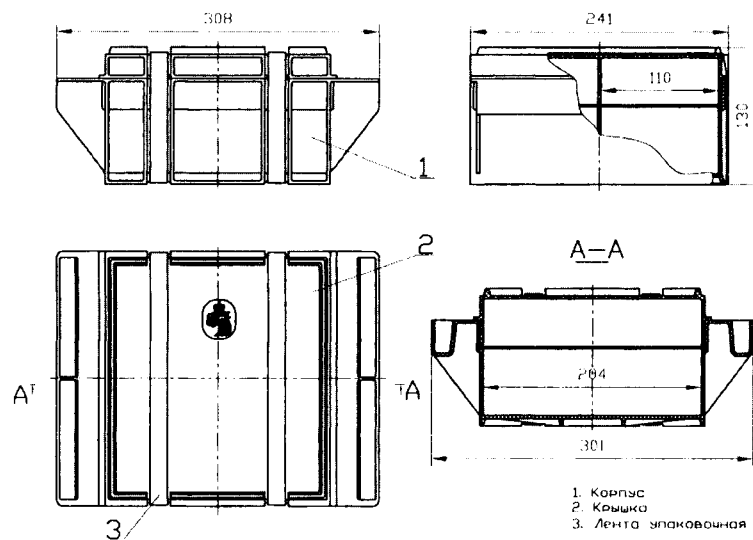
Сборочный чертеж контейнера КТ-2
